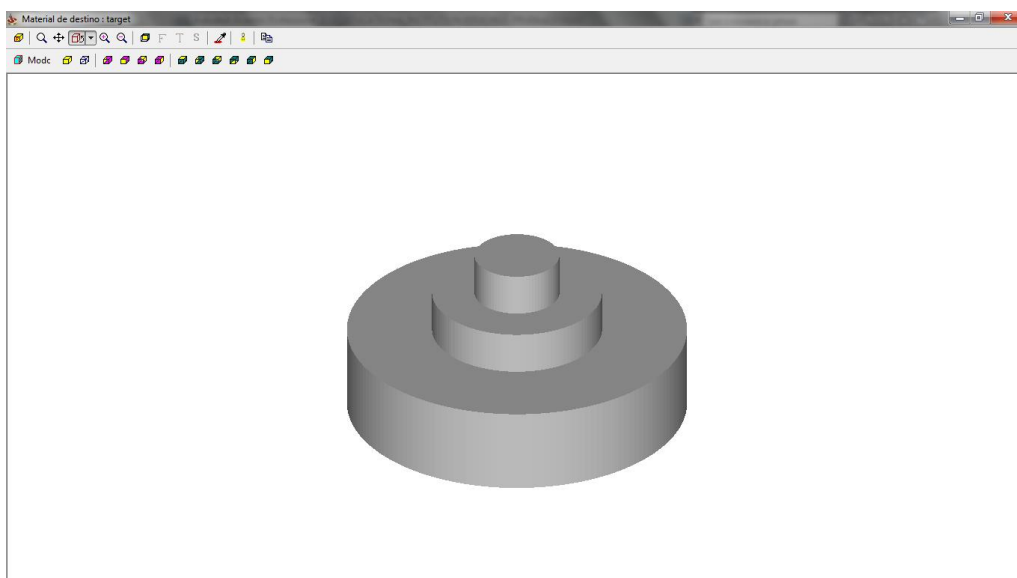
Maquinado Fresadora CNC – Vista preliminar de modelo a maquinar
